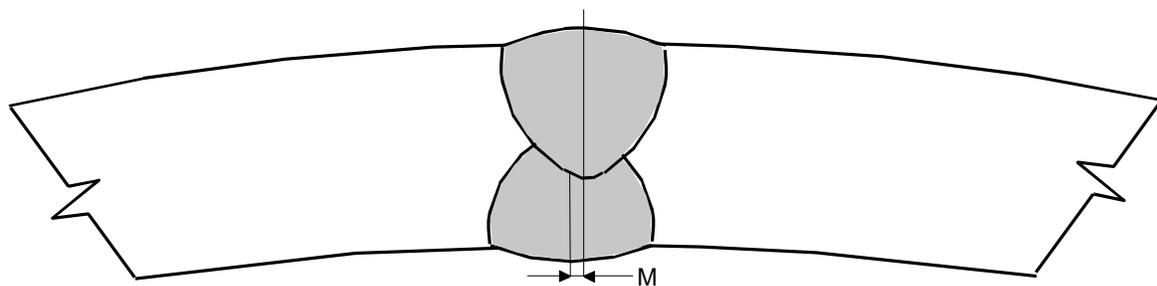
Desalineamiento de los cordones de soldadura.
